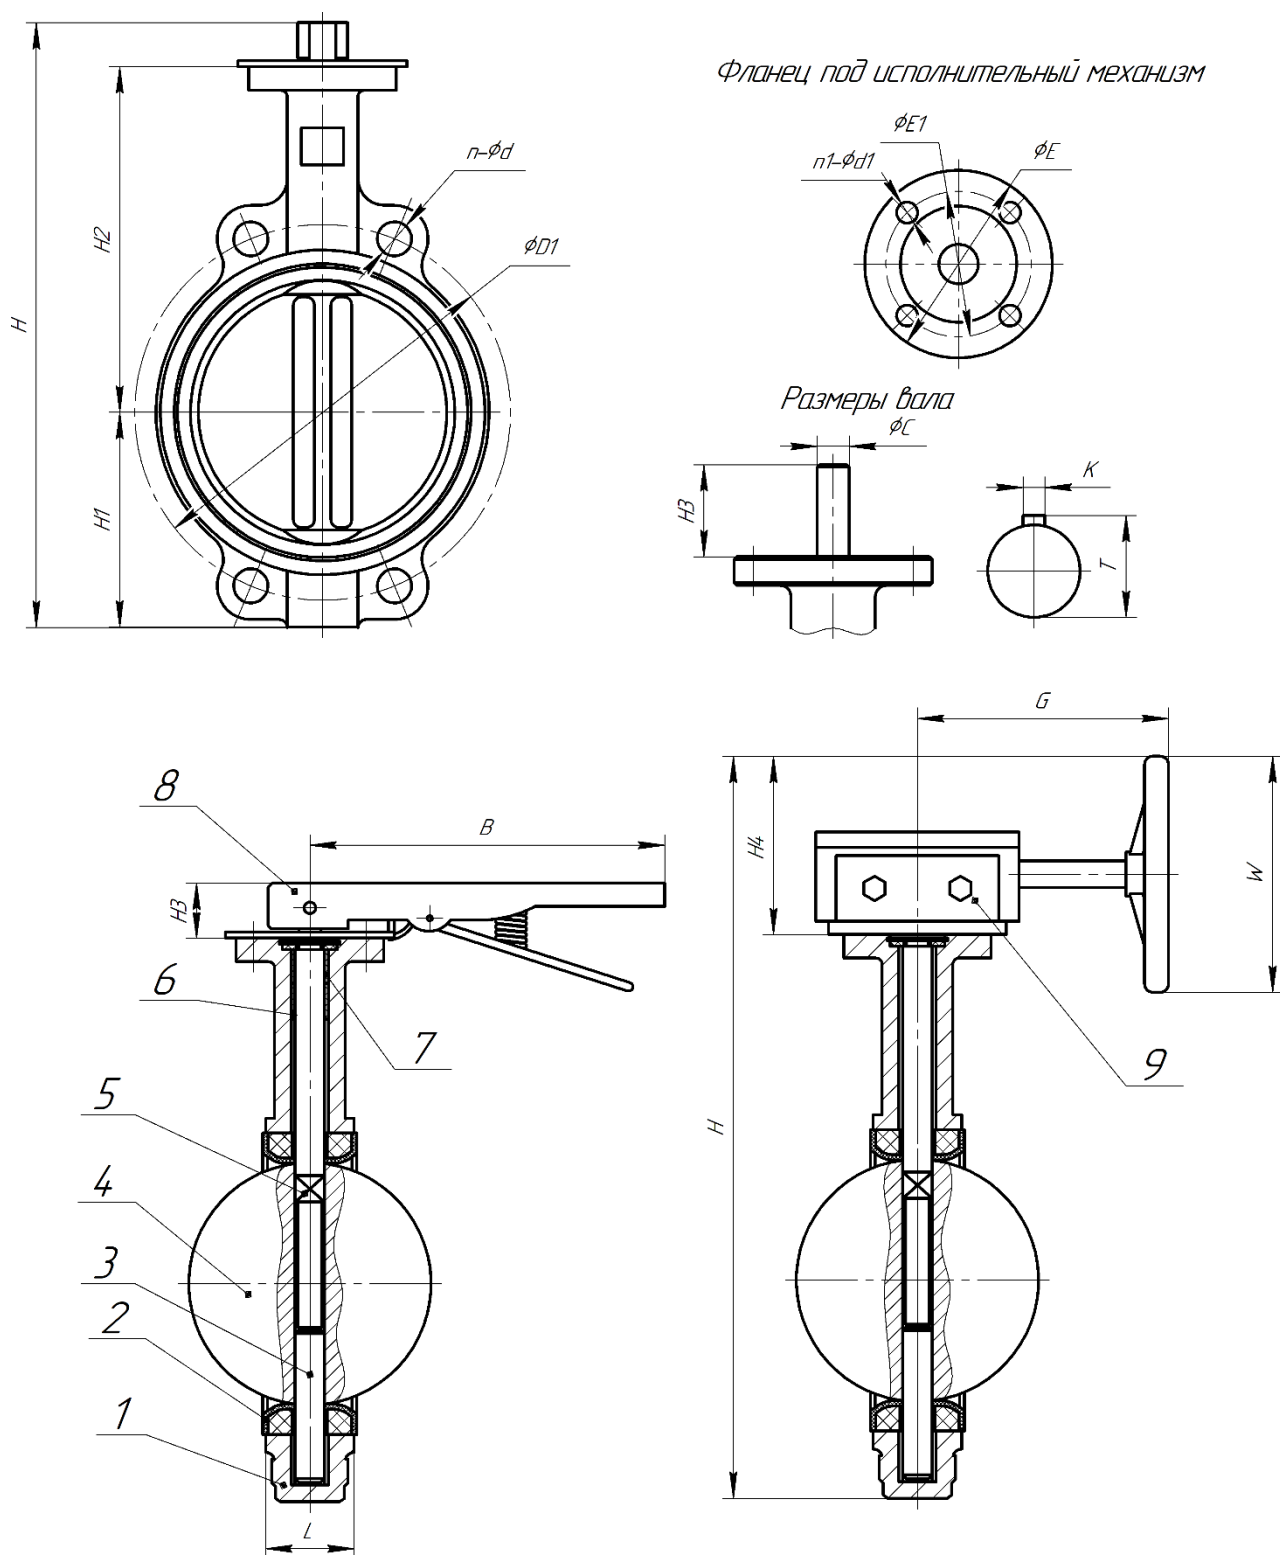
Затвор 017W.Y с рукояткой DN50-300 и редуктором DN50-350
